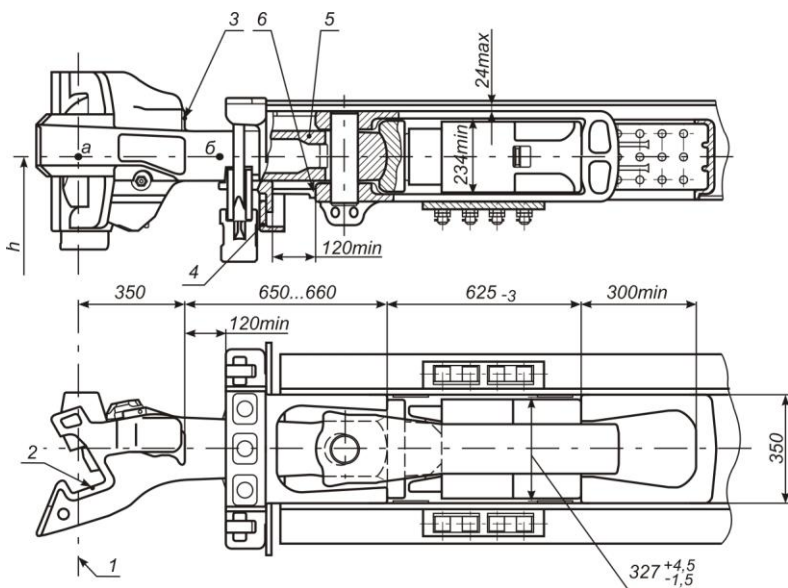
Основные установочные размеры автосцепного устройства с автосцепкой СА-3Т:
